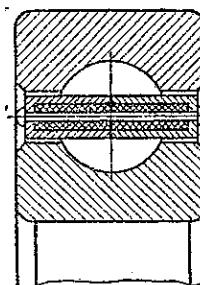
Шарикоподшипник, в сепаратор которого запрессована твердая смазка
